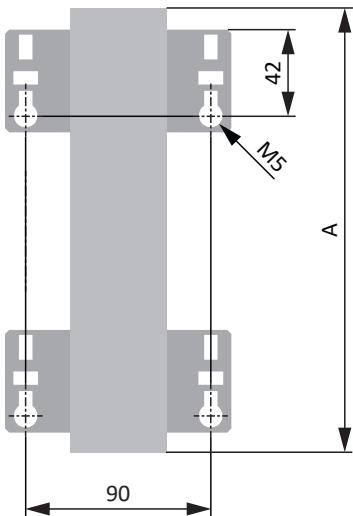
Plan de perçage KWADQU avec MWS 310L
